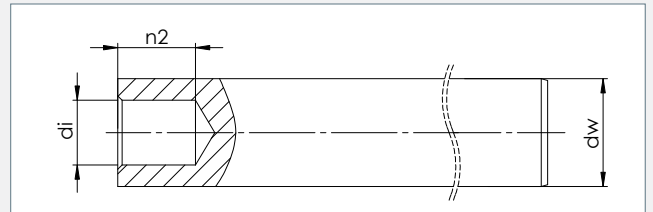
Zusammengesetzte Wellen / Compound shafts
